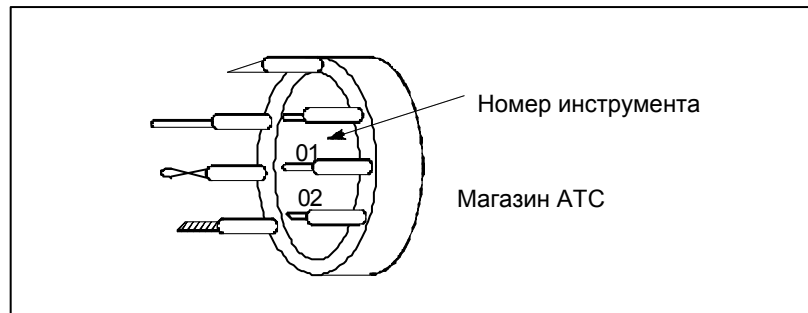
(а) Инструмент, используемый для различных видов обработки
